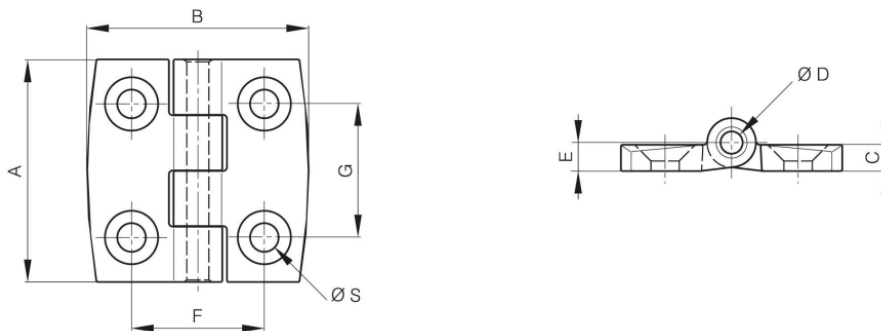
Croquis de dimensiones. Bisagra Pinet.
